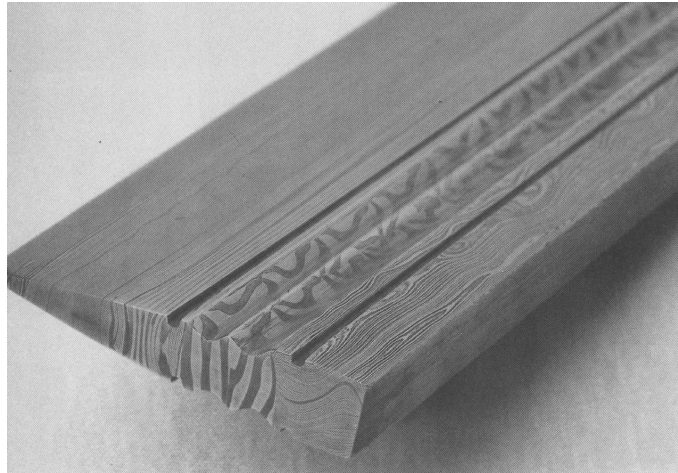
„Schweißdamast-Querschnitt“
